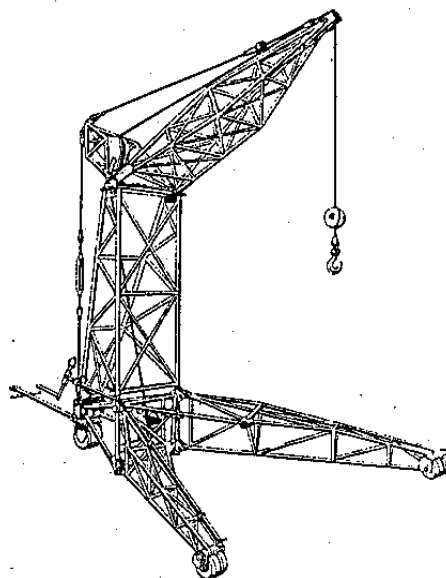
Conjunto de guincho e estrutura (talha) usado para remoção de motor.
